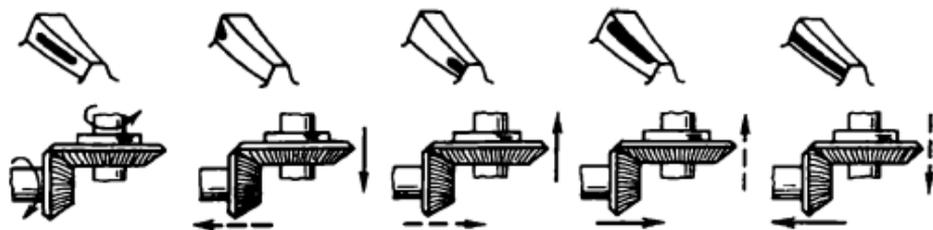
Розташування плями контакту на зубцях зубчастого колеса головної передачі
